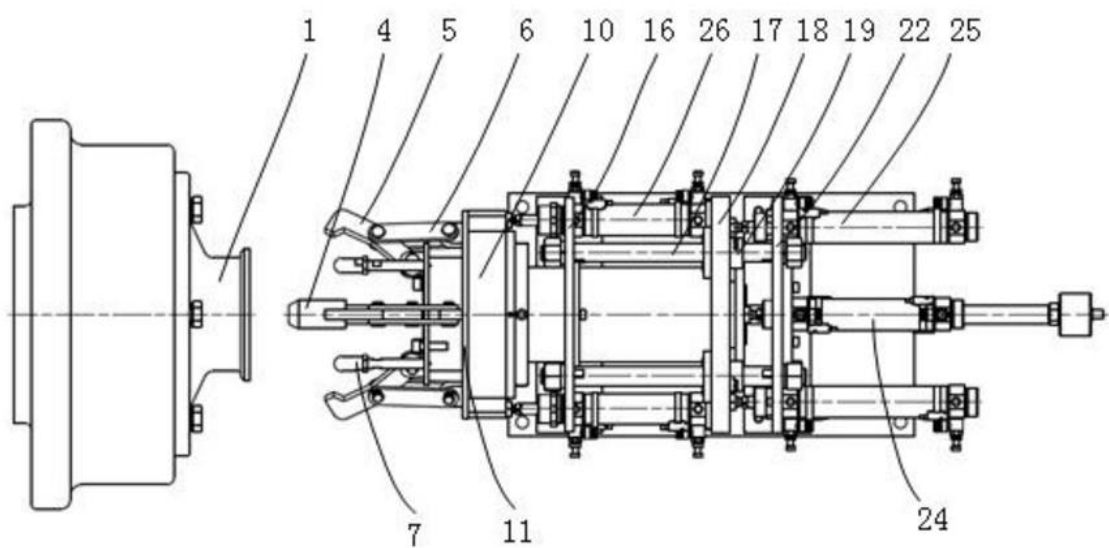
Пристрій для приєднання до колеса, вид зверху
